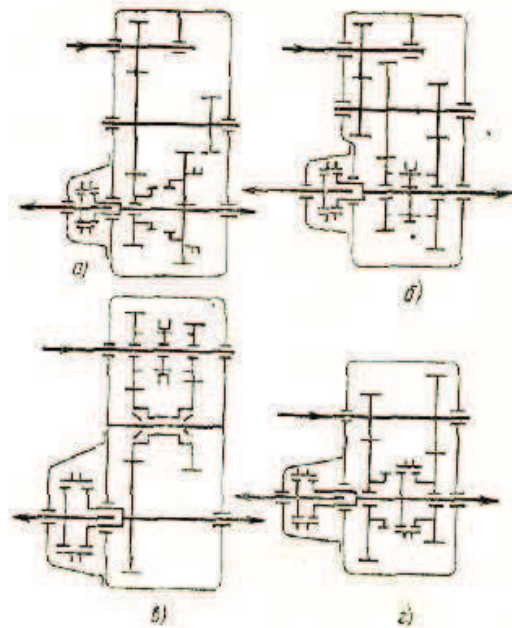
Схемы раздаточных коробок с заблокированными валами автомобилей:
